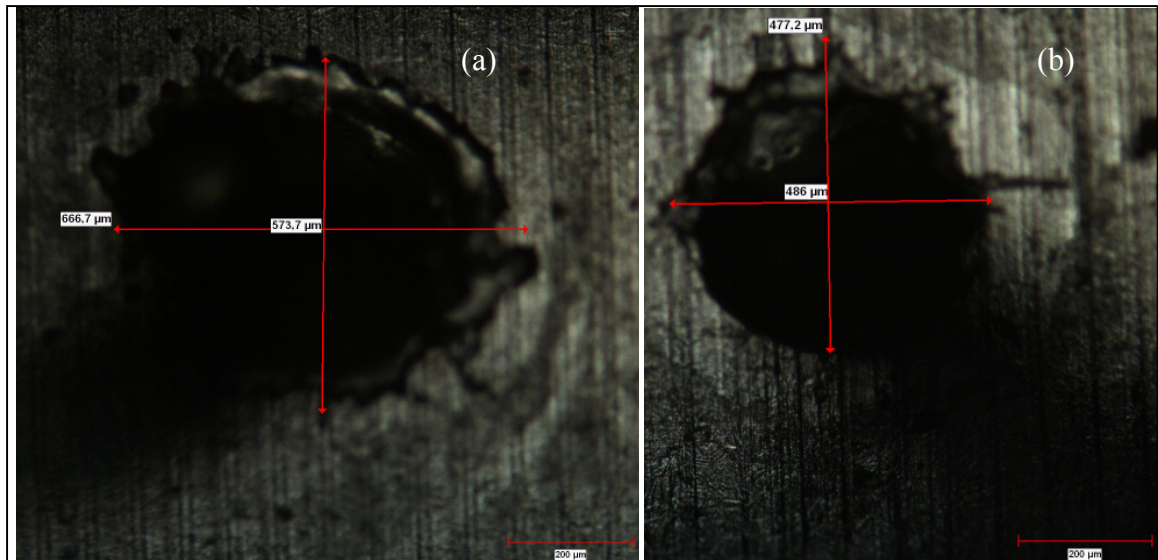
Taille de la soudure d'un fil du thermocouple après test de dilatation thermique à  $0,5\text{ }^{\circ}\text{C.s}^{-1}$  ((a) 45 HRC, (b) 22 HRC)
